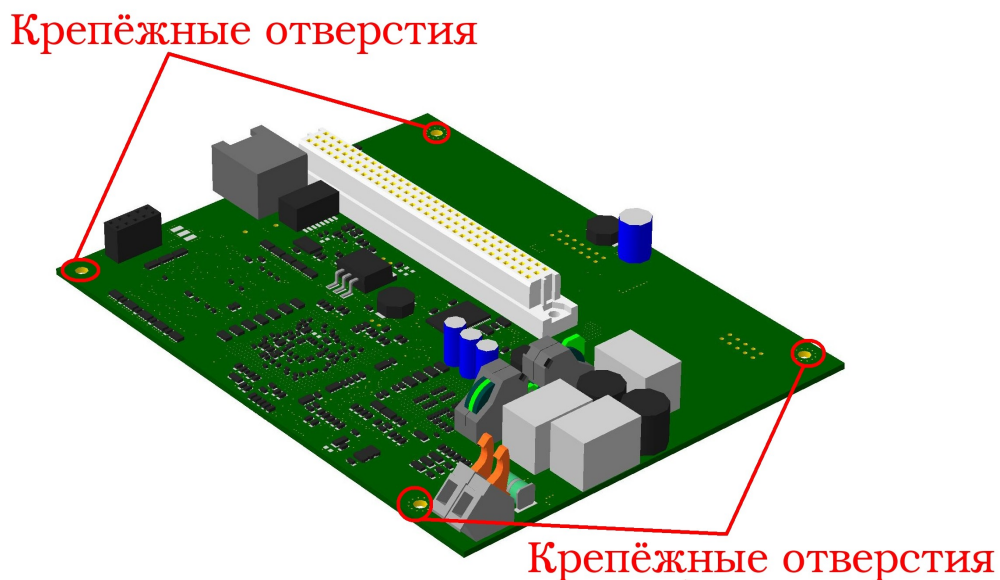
Места установки винтов для крепления АЛС-АУ в корпусе
